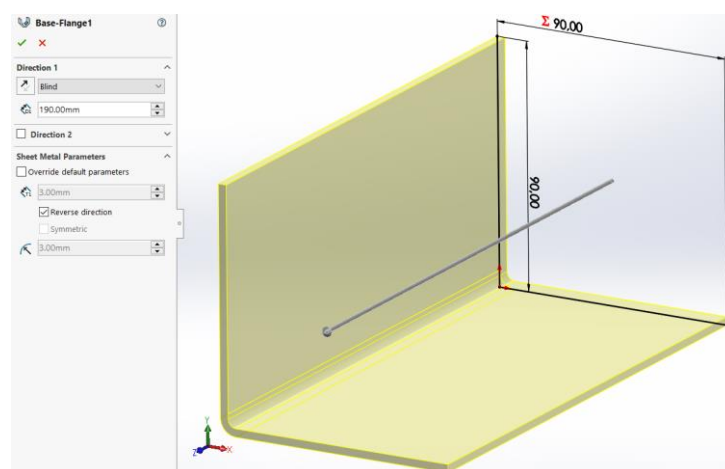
Використання інструмента Base-Flange в середовищі модуля Sheet Metal.
